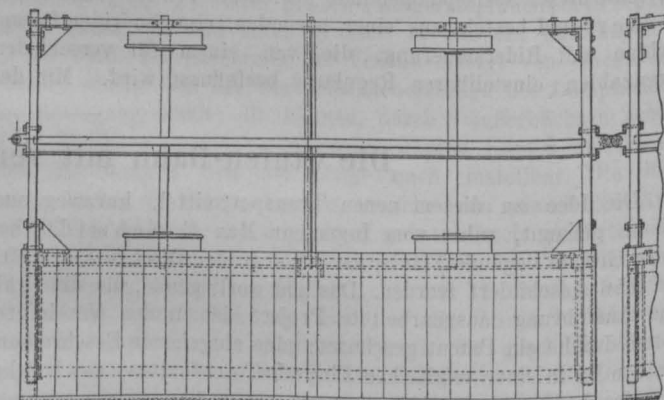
Grundriss eines Wagens der Probefahrbahn.
